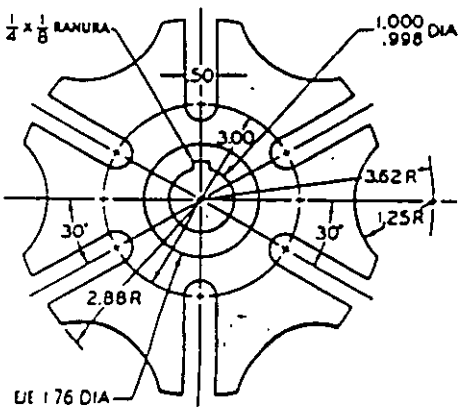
Eje de levas tipo Ginebra. Empleando el plan A-2, dibuje a lápiz. Omíta las dimensiones y las notas.
